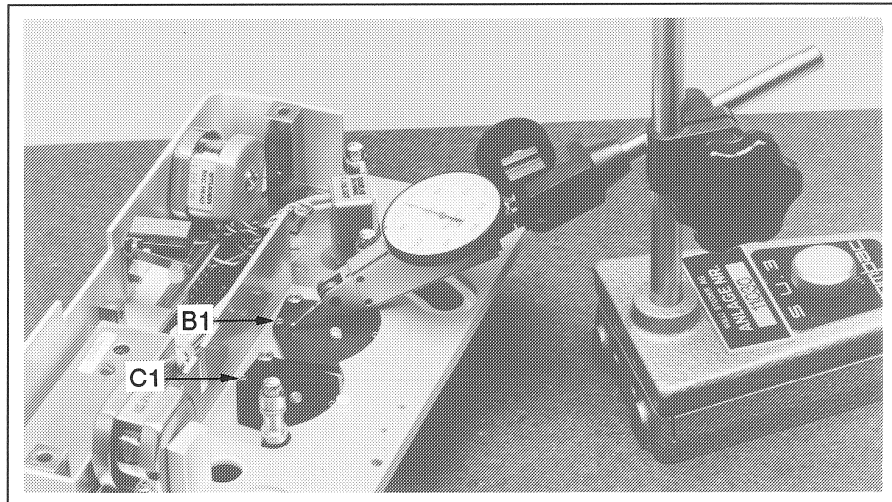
Taumelplatten einstellen: Schrauben B1, C1
